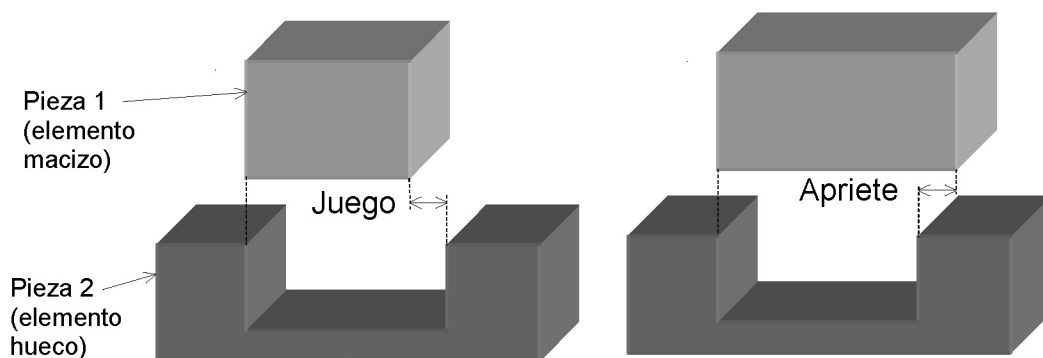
Ajuste con juego (izquierda) y con apriete (derecha)
